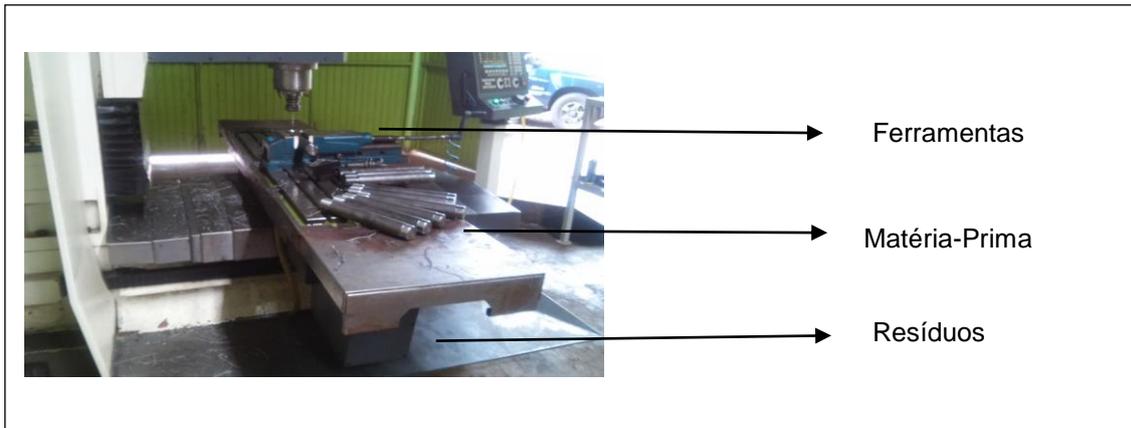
Entradas e saídas Processo Usinagem Fresadora
